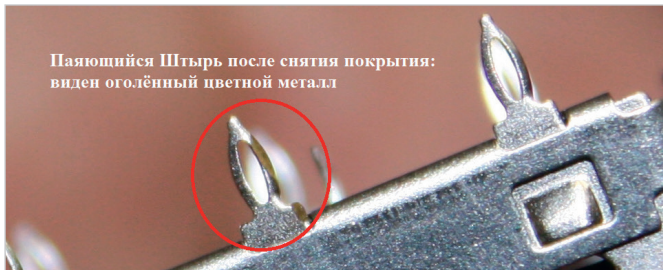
Цветной металл под покрытием паяющегося штыря Cage
